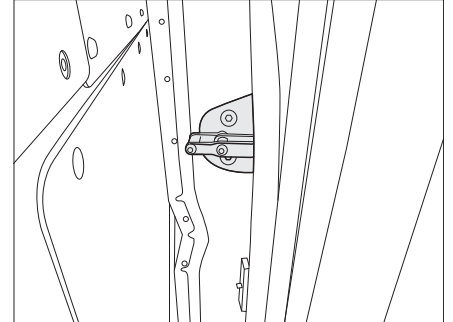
Ayuda de cierre - horquilla de cierre interior
